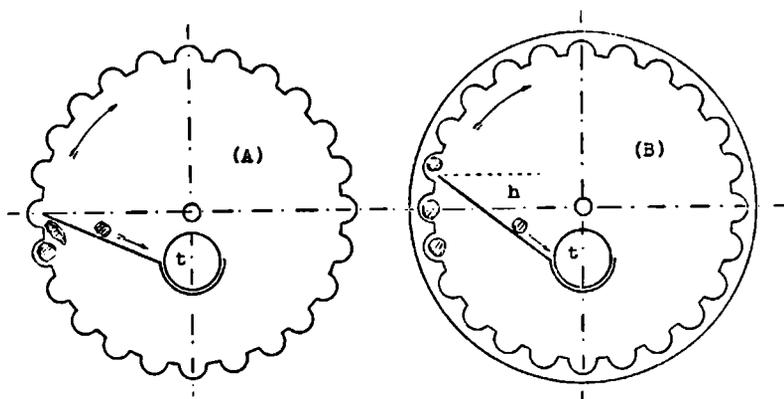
Secciones transversales esquemáticas de clasificadoras alveoladas; A, chapa estampada. B, chapa fresada
